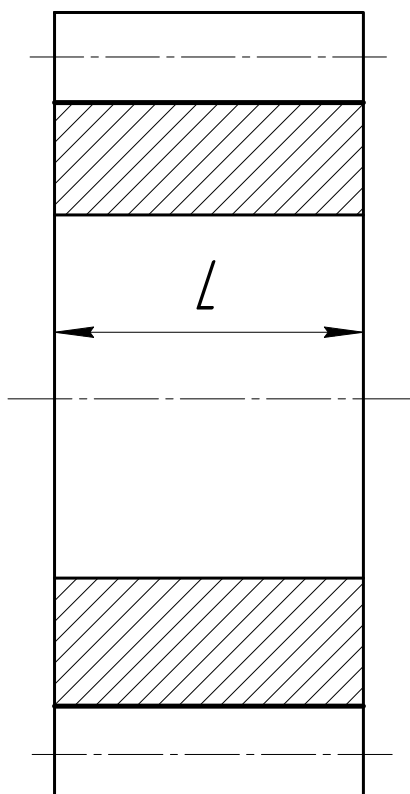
Нарезание зубчатых венцов червячными фрезами
